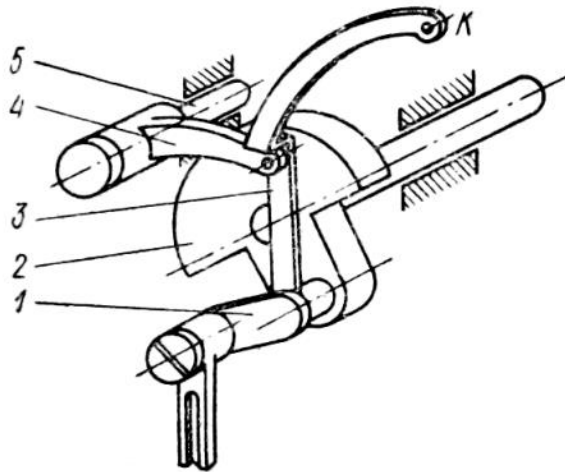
Схема четырехзвенного шарнирно-рычажного механизма нитепритягивателя
